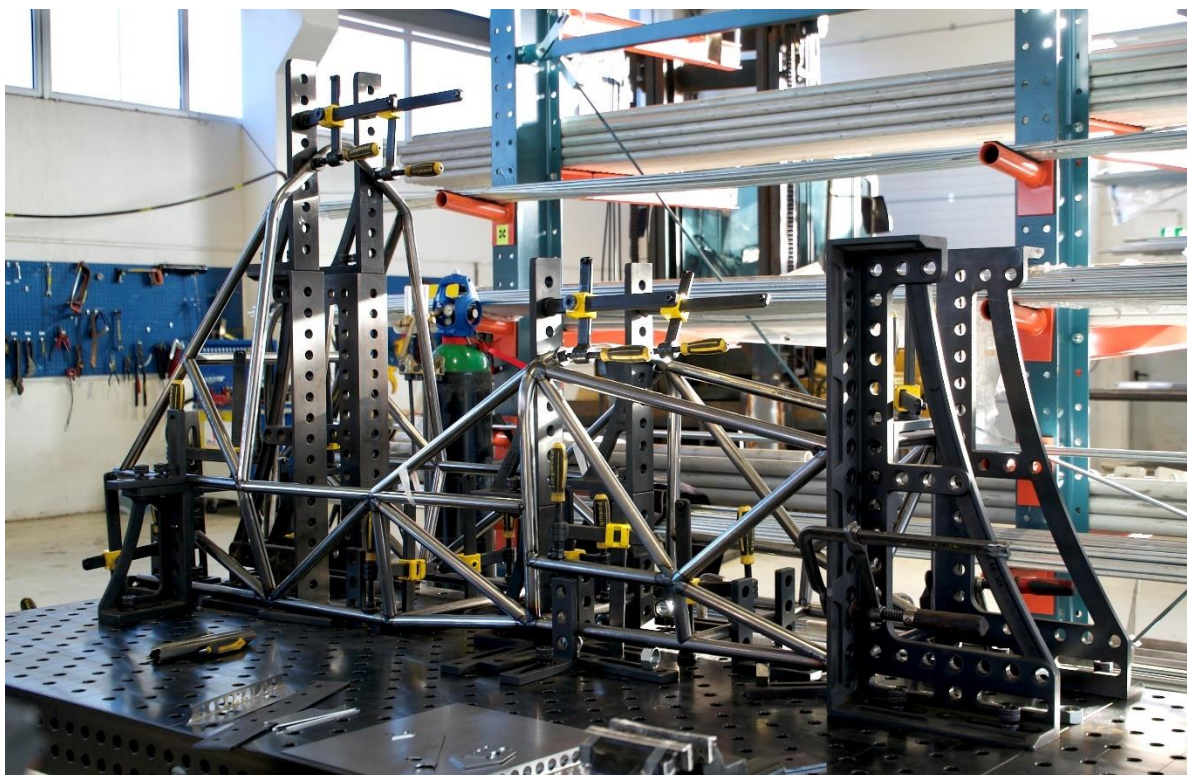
стапель для сварки пространственной металлической рамы гоночного болида «Формула Студент»
